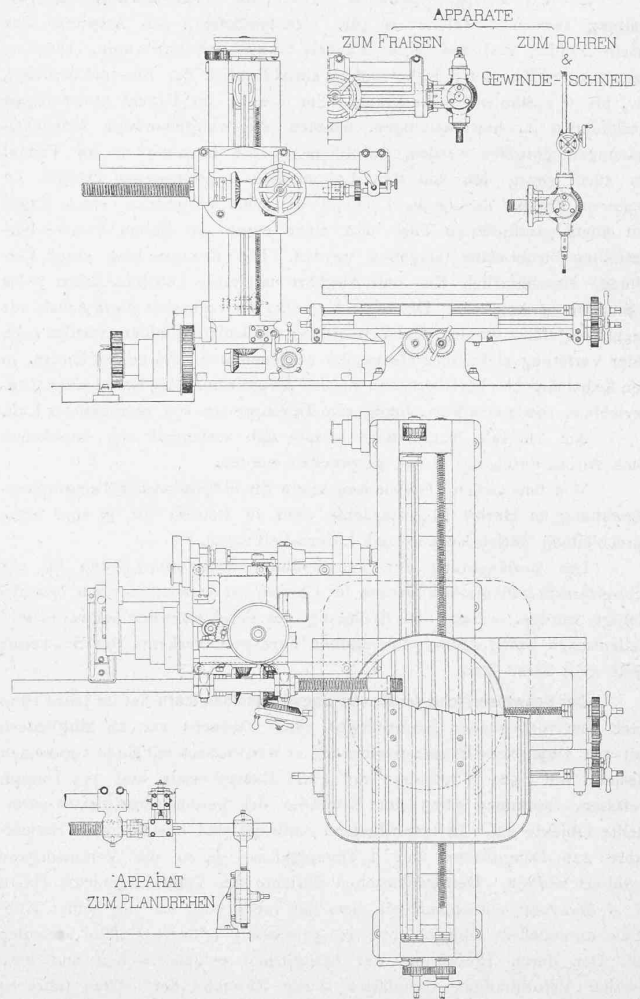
Universal-Fräsmaschine. — Masstab 1 : 50.
